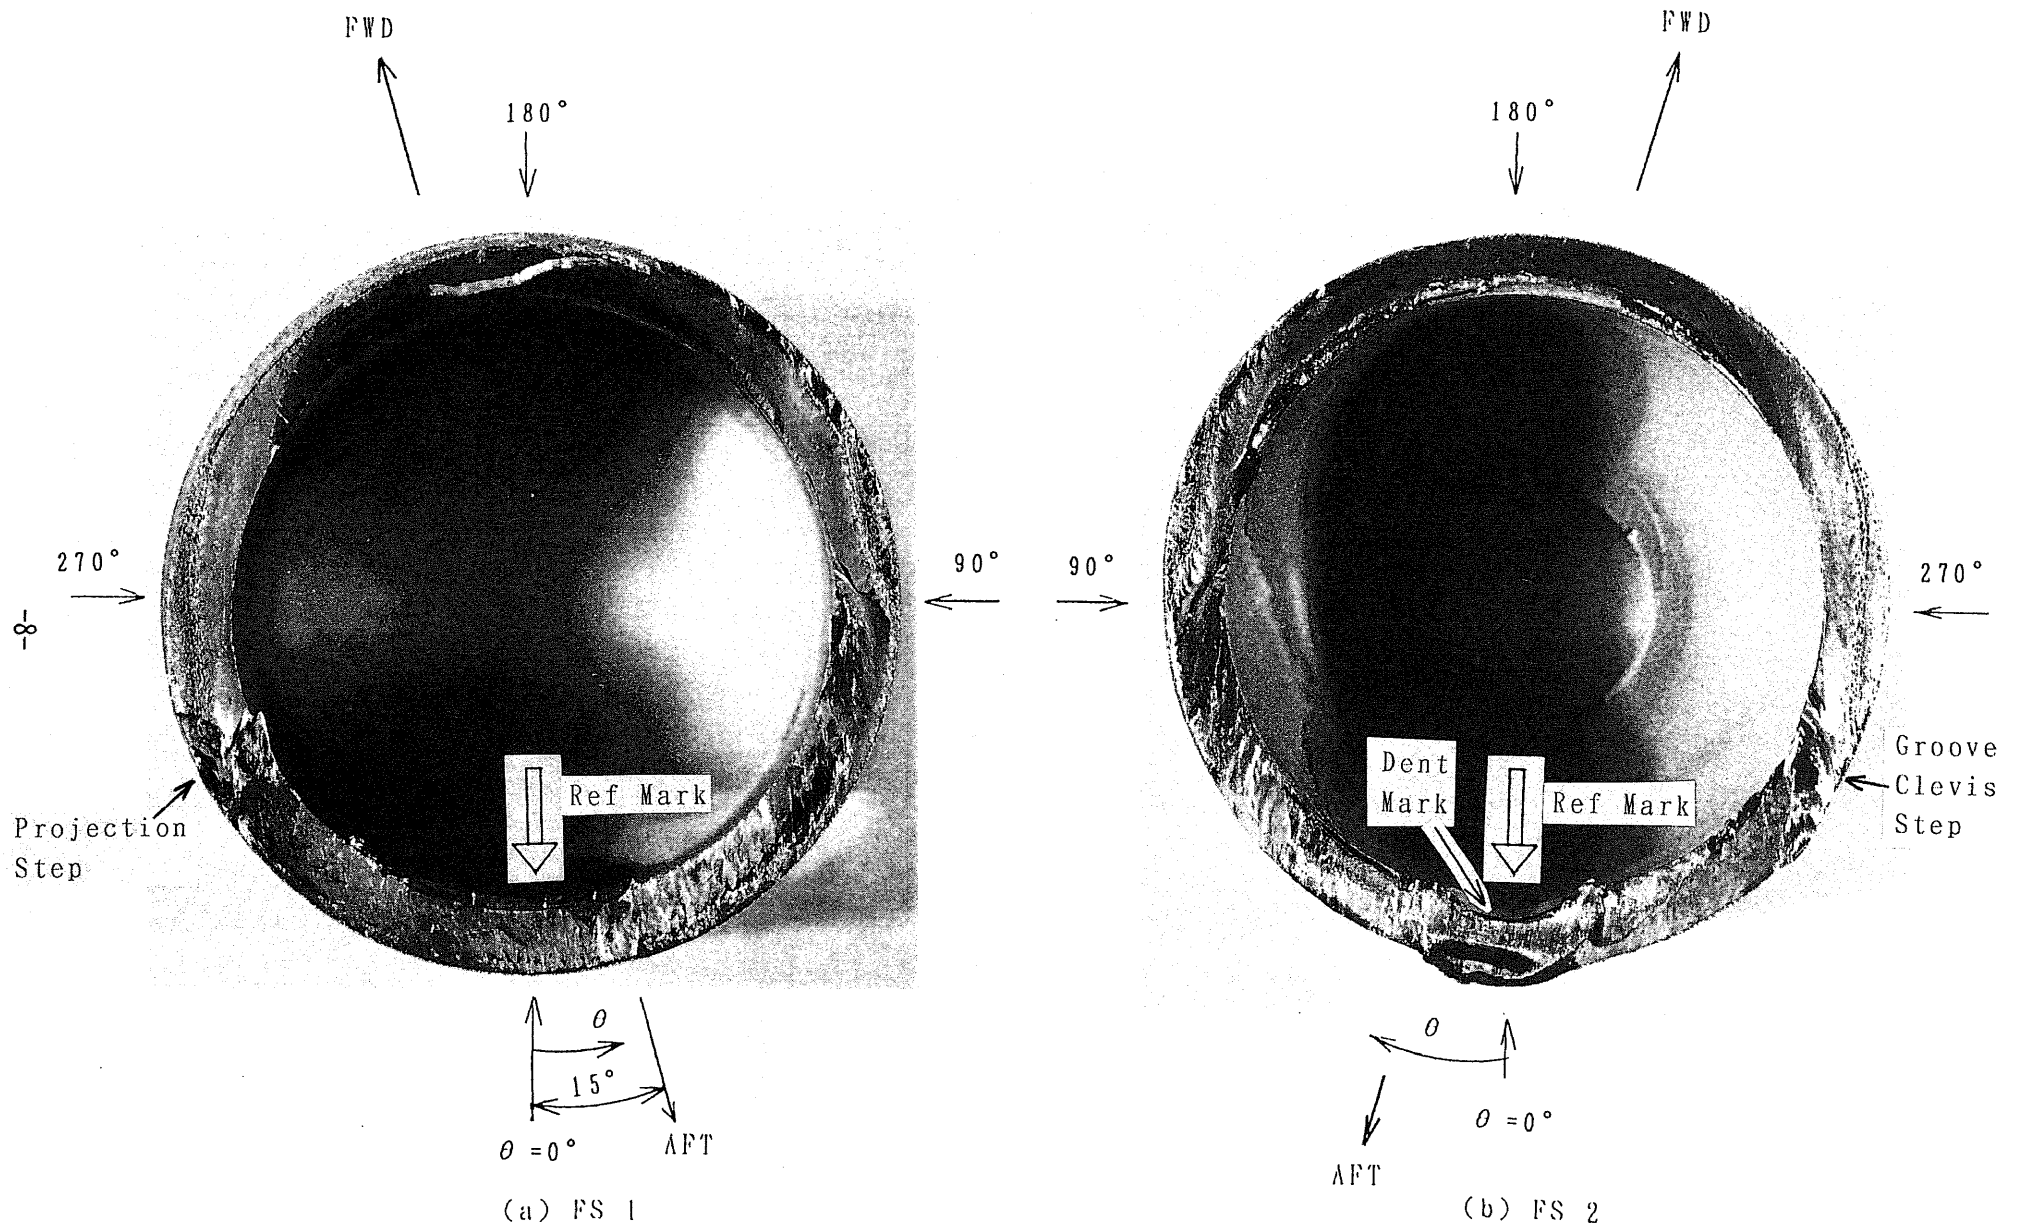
Upper Link FWD Fuse Pin 破面のマクロ観察(その1、FS1と2)
